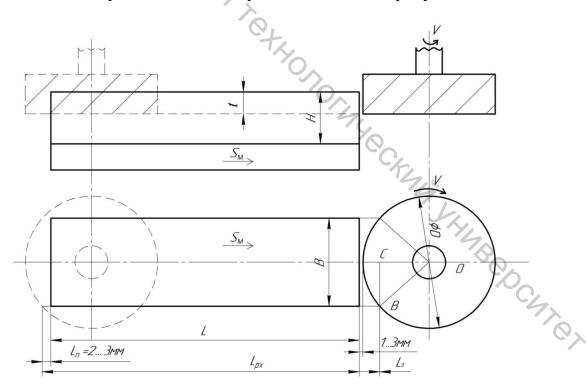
Схема определения длины рабочего хода для торцевых и концевых фрез при симметричном фрезеровании
